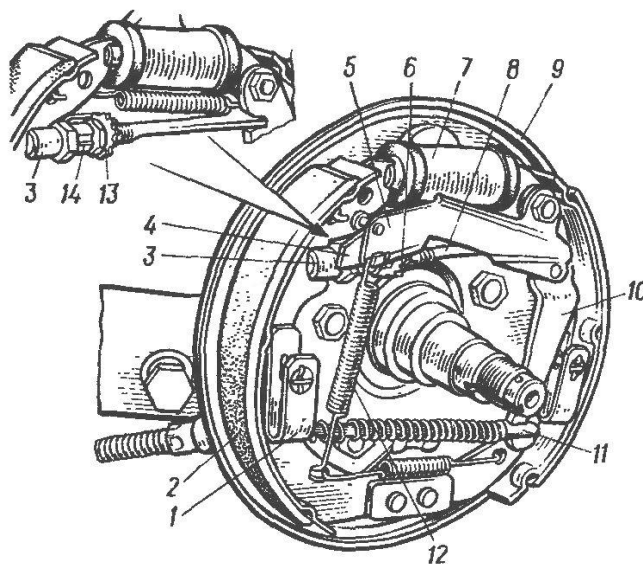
Колесный цилиндр автомобиля ВАЗ-2106 с устройством автоматической регулировки зазора
